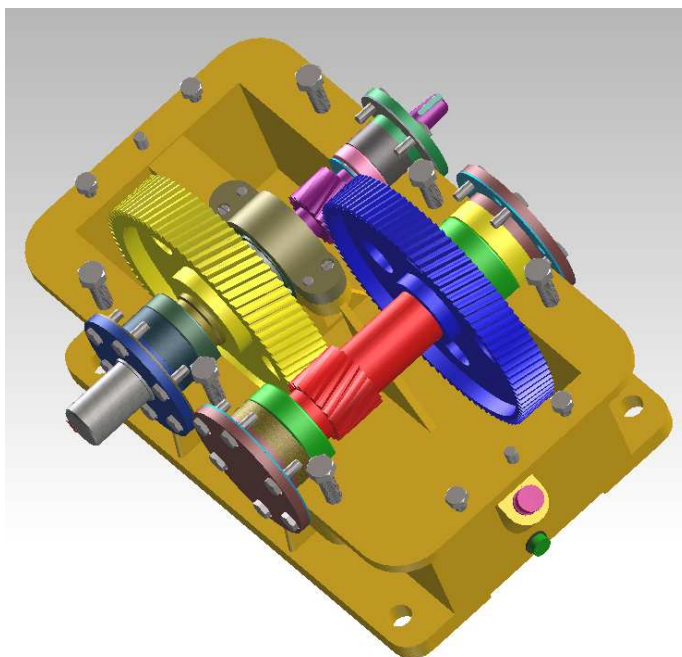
Модель цилиндрического редуктора в 3D-формате
